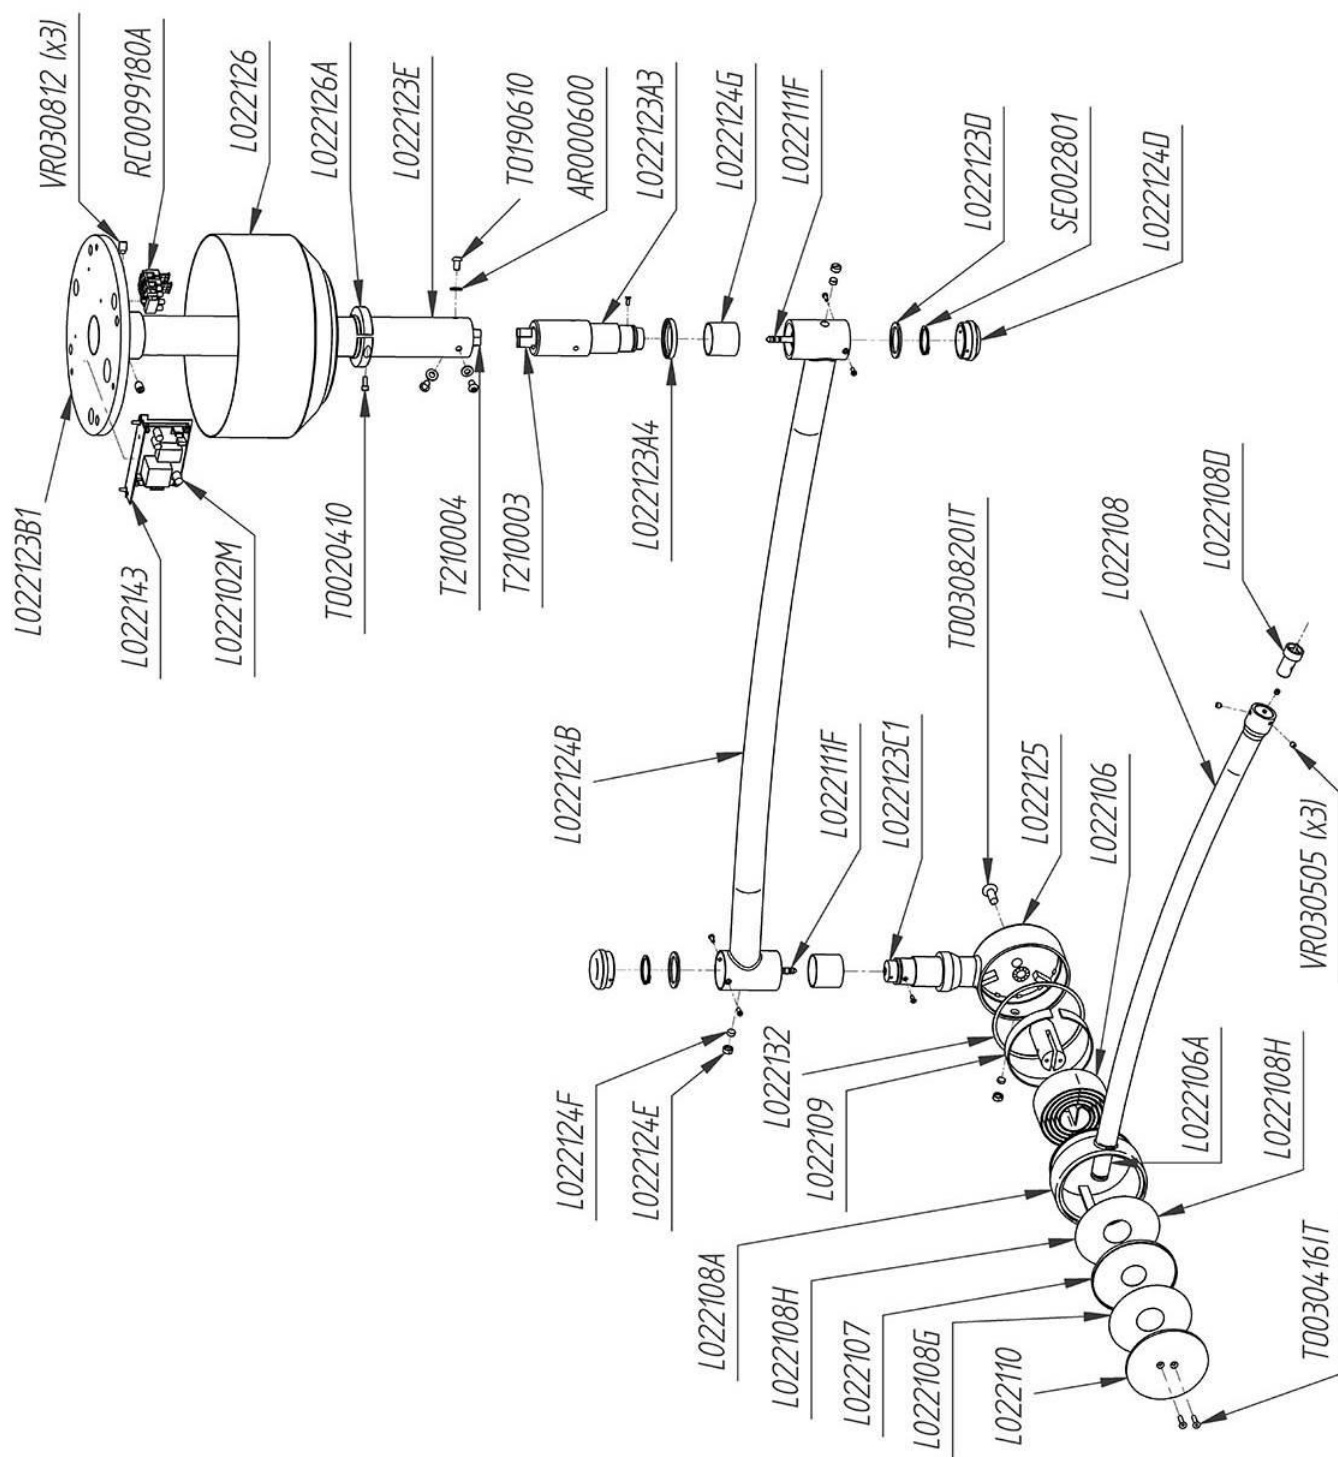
Despiece de brazos y anclaje a techo / Exploded view of the arms and ceiling mount.
